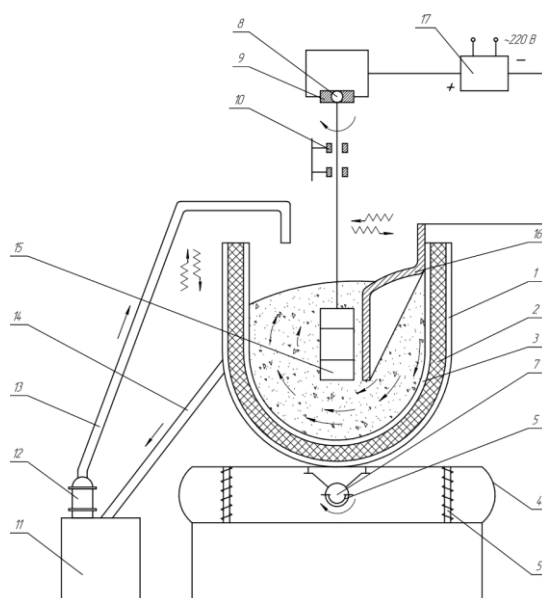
Схема процесса электрохимического виброабразивной обработки: 1 – обшивка контейнера стальная; 2 – резиновая облицовка; 3 – внутренняя облицовка из нержавеющей стали; 4 – ленточная пружина; 5 – спиральная пружина; 6 – груз; 7 – вал с несбалансированным грузом; 8 – токосъемное кольцо; 9 – щетки меднографитовые; 10 – текстолитовые подшипники; 11 – бак с электролитом; 12 – насос; 13 – шланг подачи электролита; 14 – шланг отлива электролита; 15 – набор обрабатываемых деталей; 16 – катод; 17 – выпрямитель
